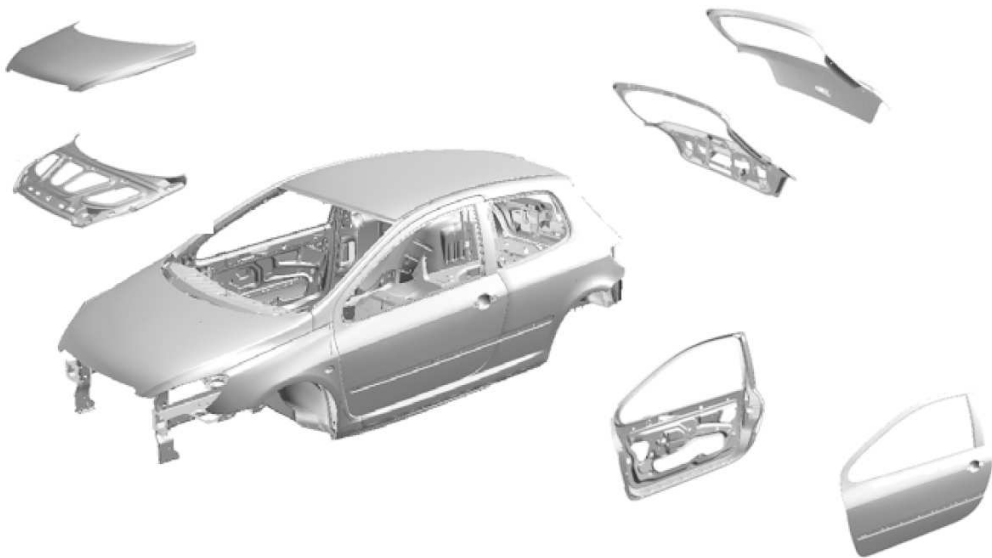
Exemples d'ouvrants sur un véhicule qui sont assemblés par sertissage.
